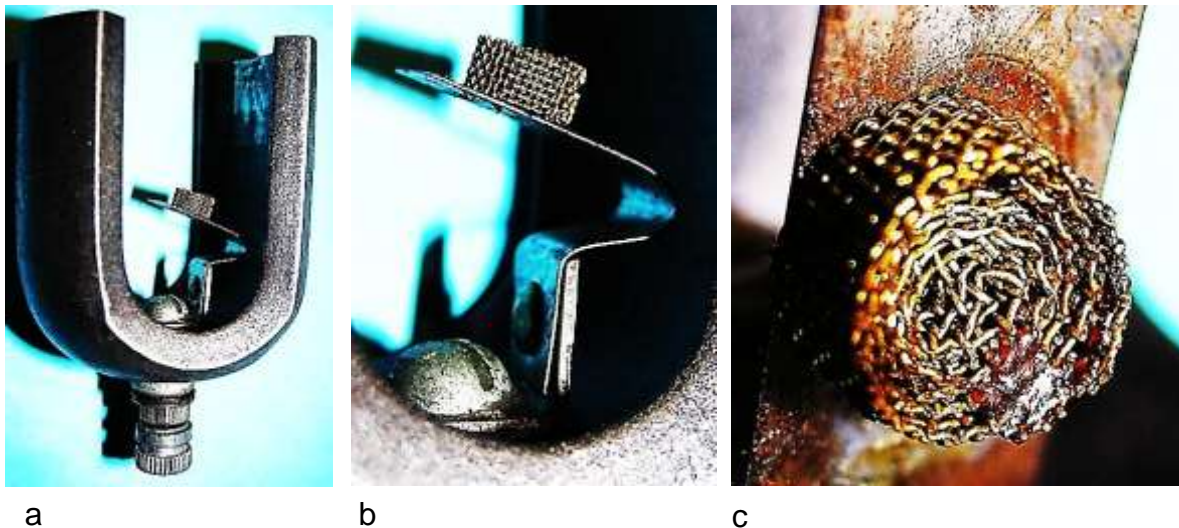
Spannung führender Kontakt: a) Tulpenmagnet mit Kabelanschlussbolzen
